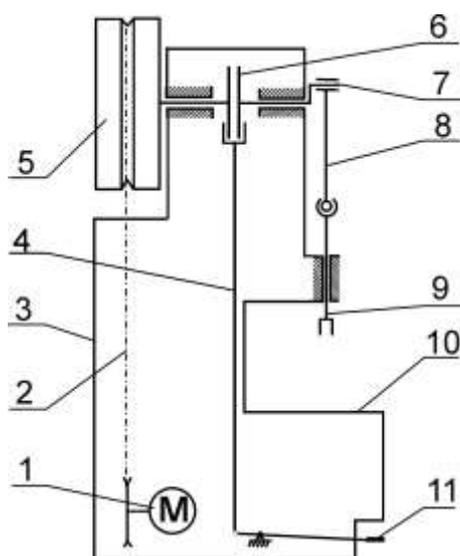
Конструктивна схема кривошипного преса: 1 – електродвигун;
